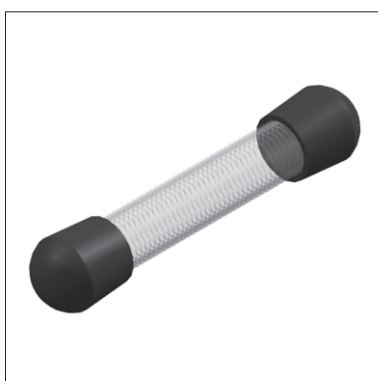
Защитная заглушка из полимерного материала для резьбовых штифтов
